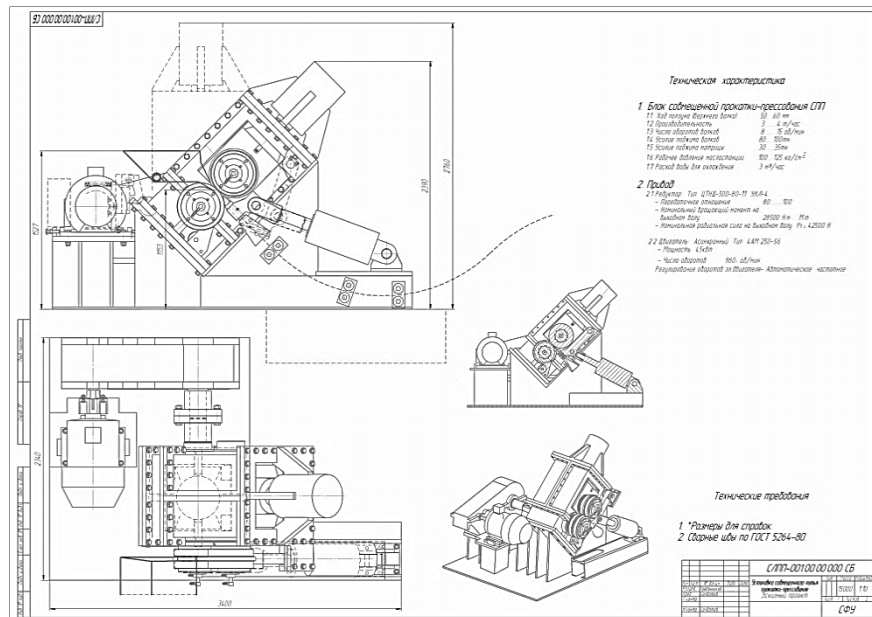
Рабочий чертеж установки СЛИПП-2,5
